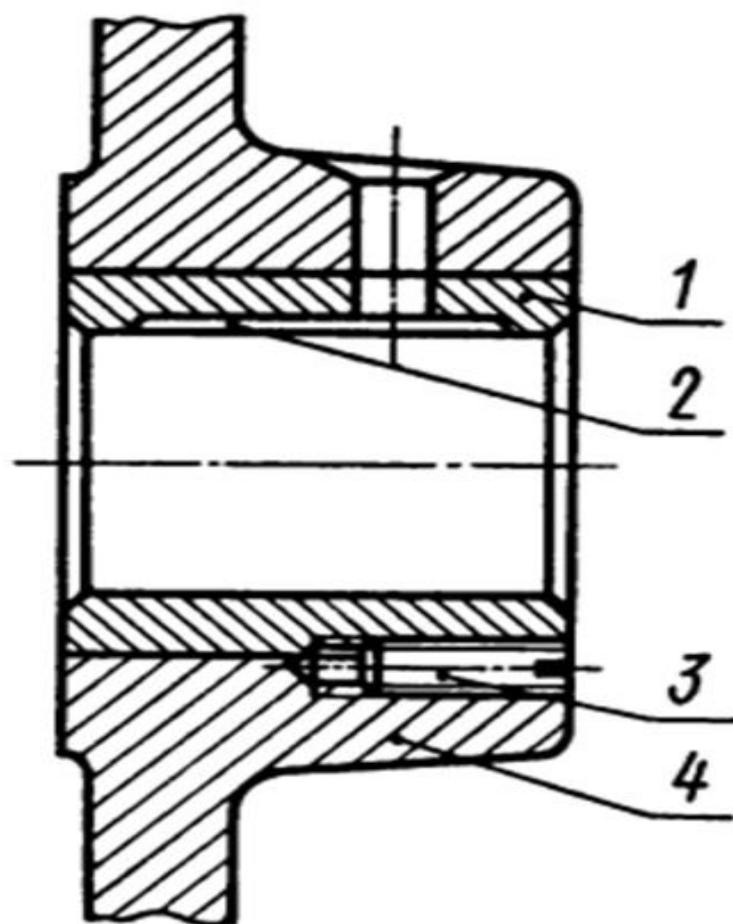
Неразъемный подшипник, встроенный в станину машины:
